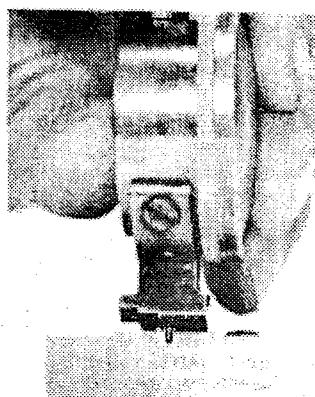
Установочный эталон калибра высоты резьбы безмуфтового соединения
